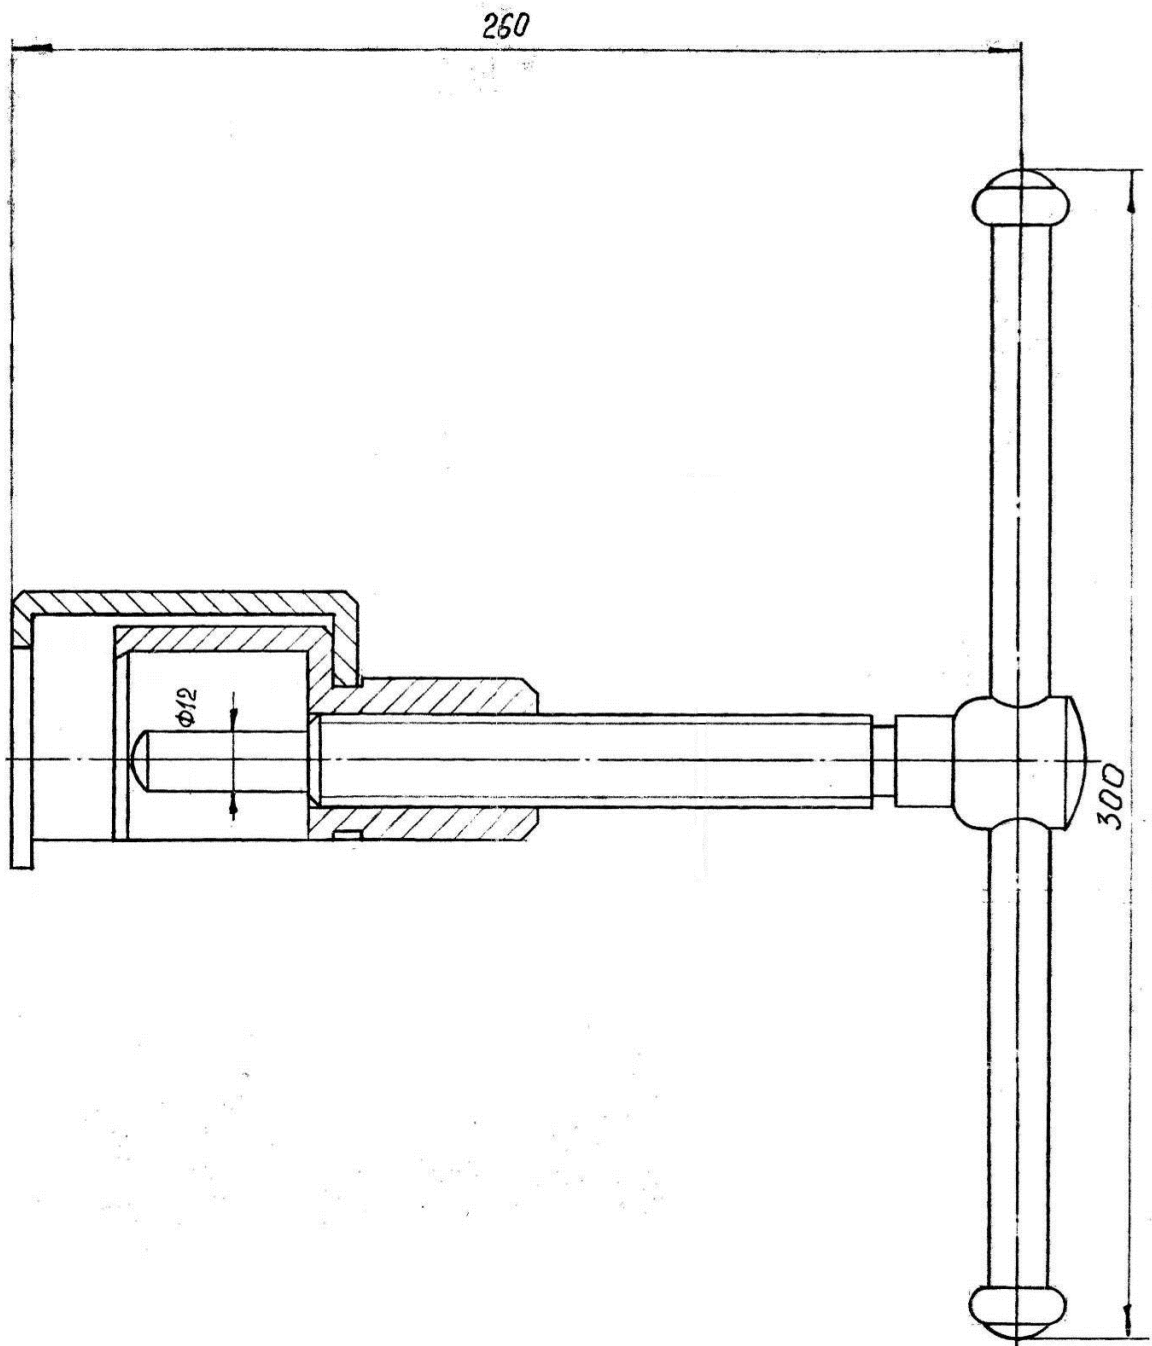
ЗМ 7814-5118 – Съемник звездочки коленчатого вала
